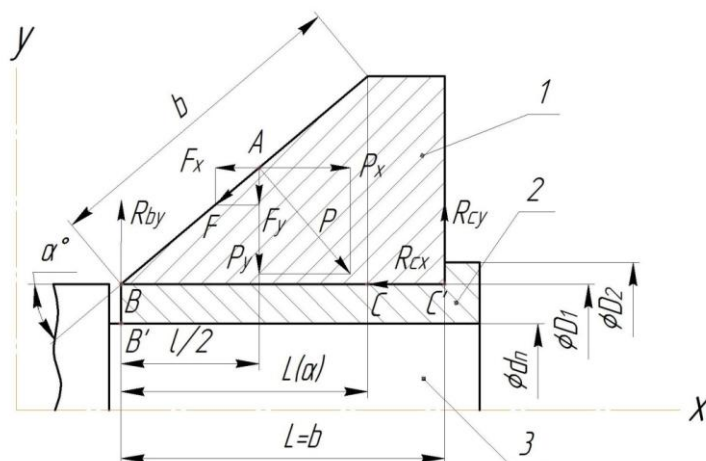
Схема действие сил на коническом формующем элементе и реакции опор на подшипнике: 1 – конический элемент; 2 – подшипник; 3 – вал вала
